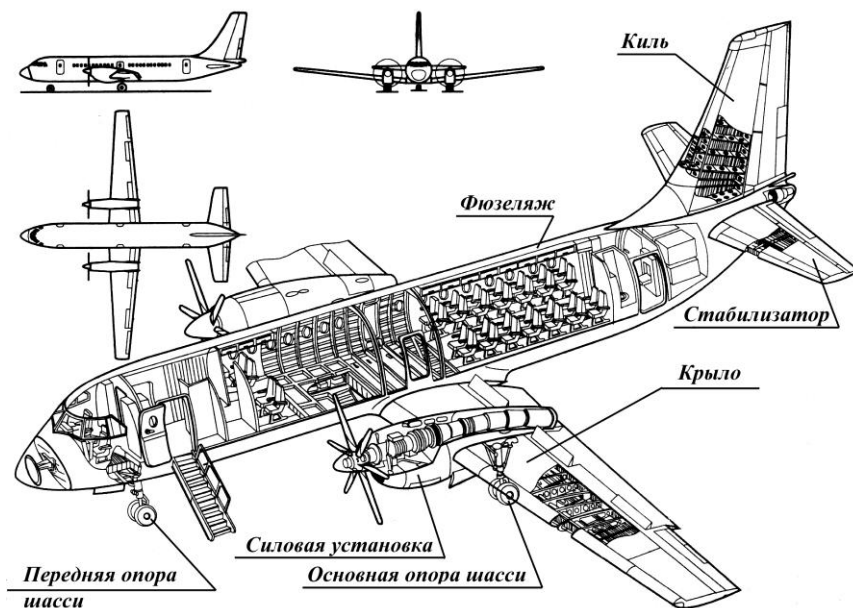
Внешний вид и компоновка самолёта Ил-114.
